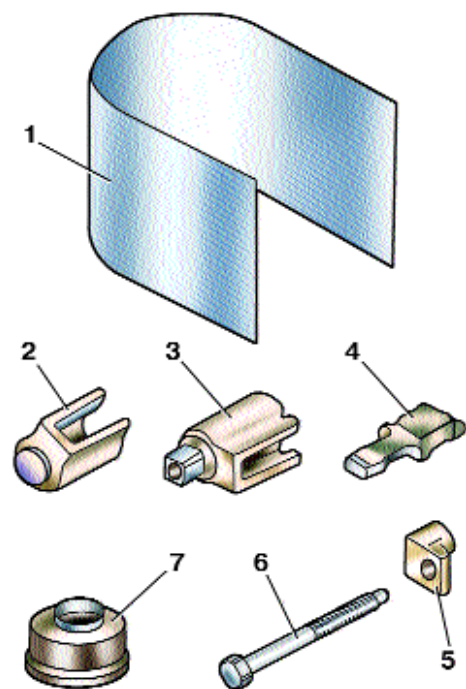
Комплект уплотнителей, изоляторов и крепежных деталей (77 01 203 879): 1 – защитная лента; 2, 3, 4 – изоляционные чехлы клемм; 5 – изоляционная втулка; 6 – винт крепления изоляционной втулки; 7 – пылезащитный чехол подшипника
